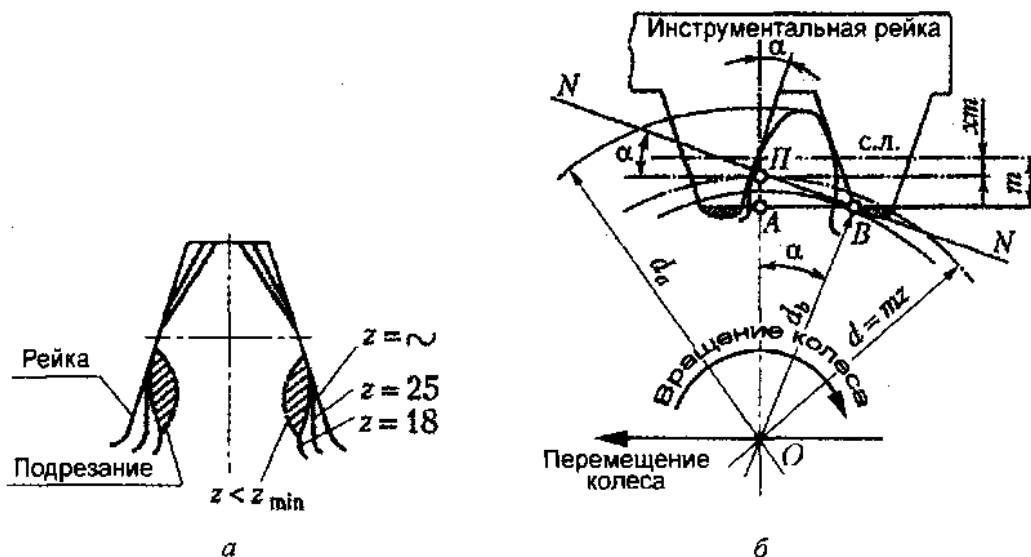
Зацепление зубчатого колеса с рейкой
